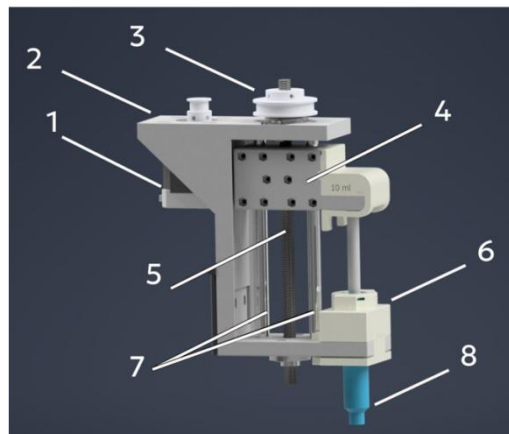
Конструкция экструдера для 3D-печати вязкими «чернилами»: 1 – шаговый двигатель; 2 – корпус; 3 – ременный редуктор; 4 – поршень; 5 – резьбовой вал; 6 – линейные направляющие; 7 – держатель для емкости; 8 – емкость с «чернилами»
